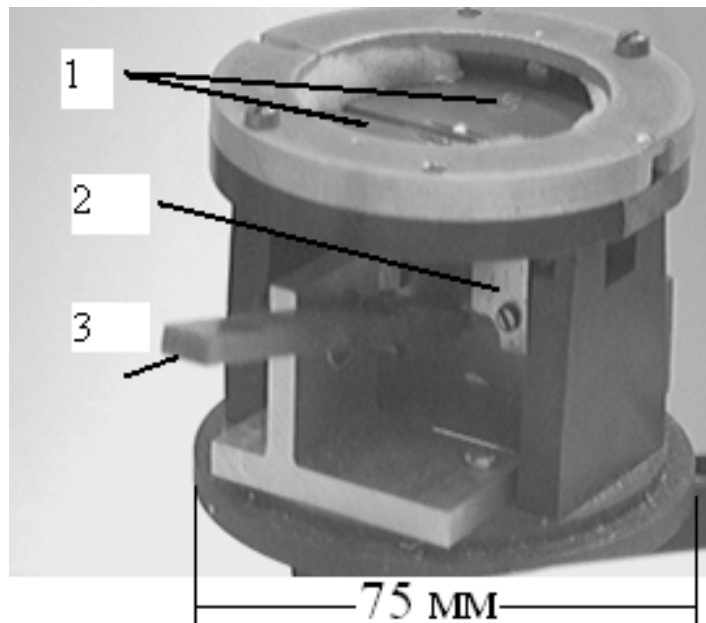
Фотография столика в установке лазерного скрайбирования, позволяющего раскалывать пластины с КМ и ФП после формирования канавки. 1 – шарнирные поверхности с вакуумными присосками; 2 – подвижный клин; 3 – ручка толкателя клина.
